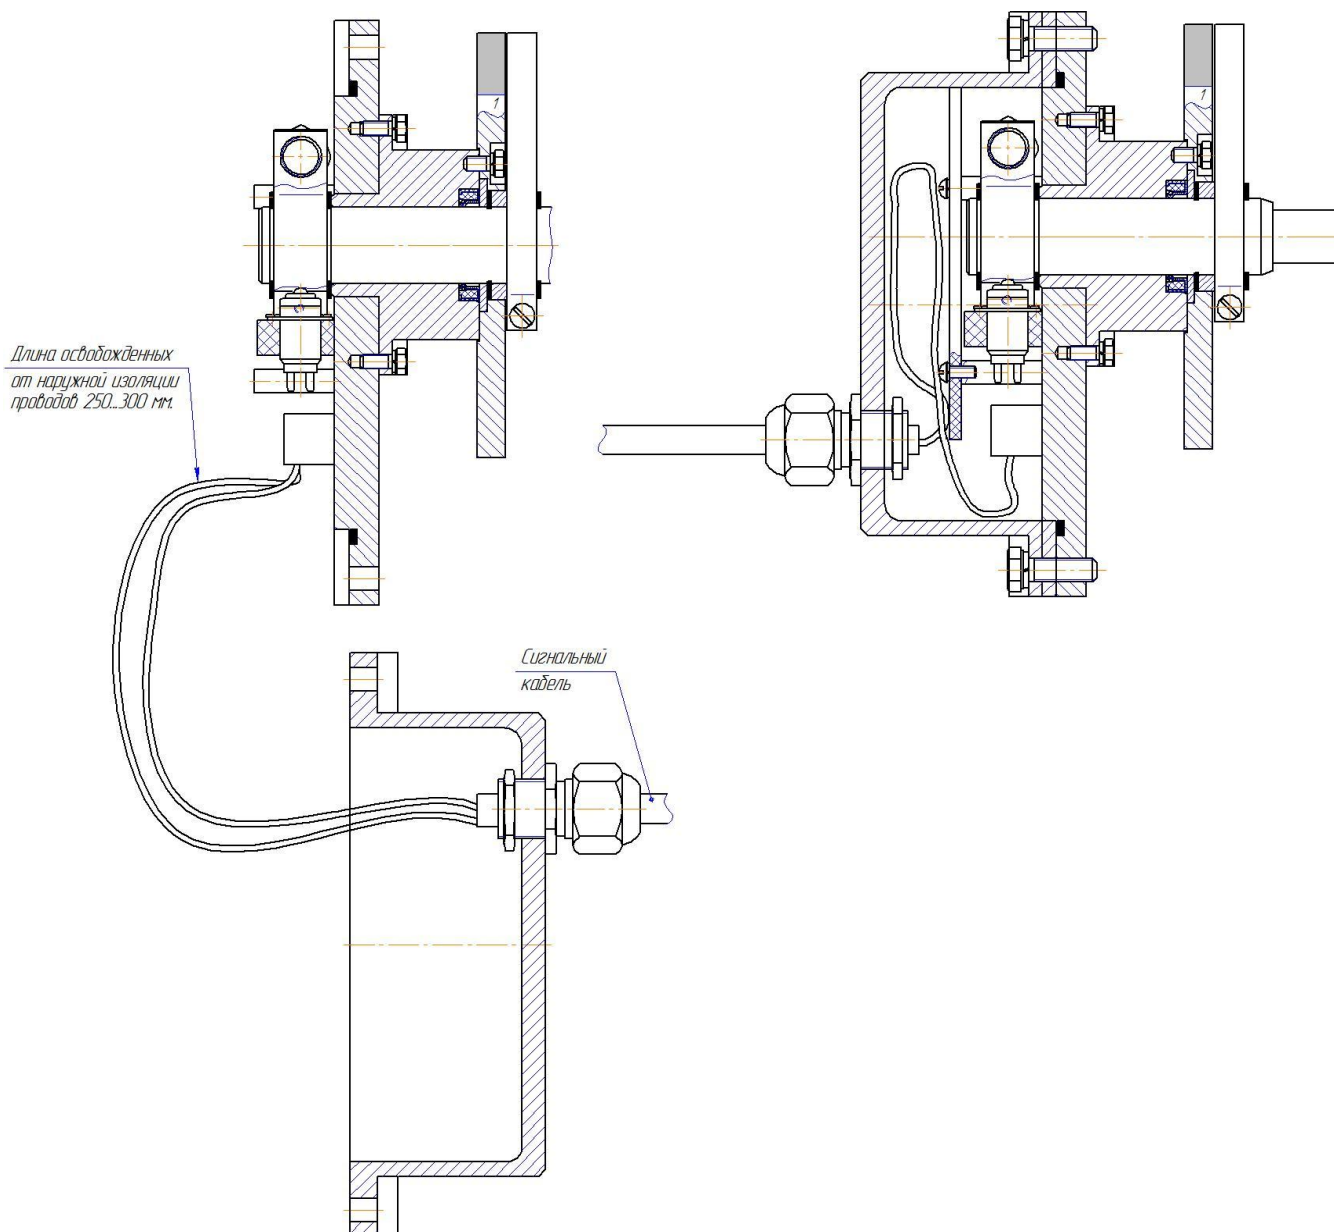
монтаж кабеля и его укладка при установке крышек
